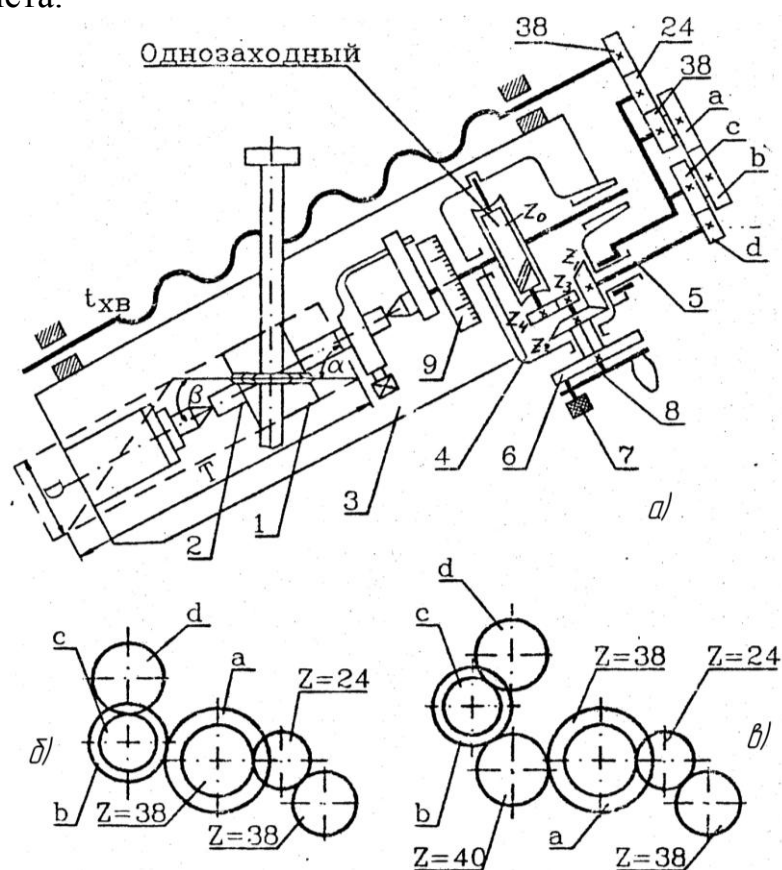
Схемы: *a* — наладки фрезерного станка на получение спиральных поверхностей; *б, в* — расположения сменных зубчатых колес с учетом направления фрезеруемых винтовых канавок,
